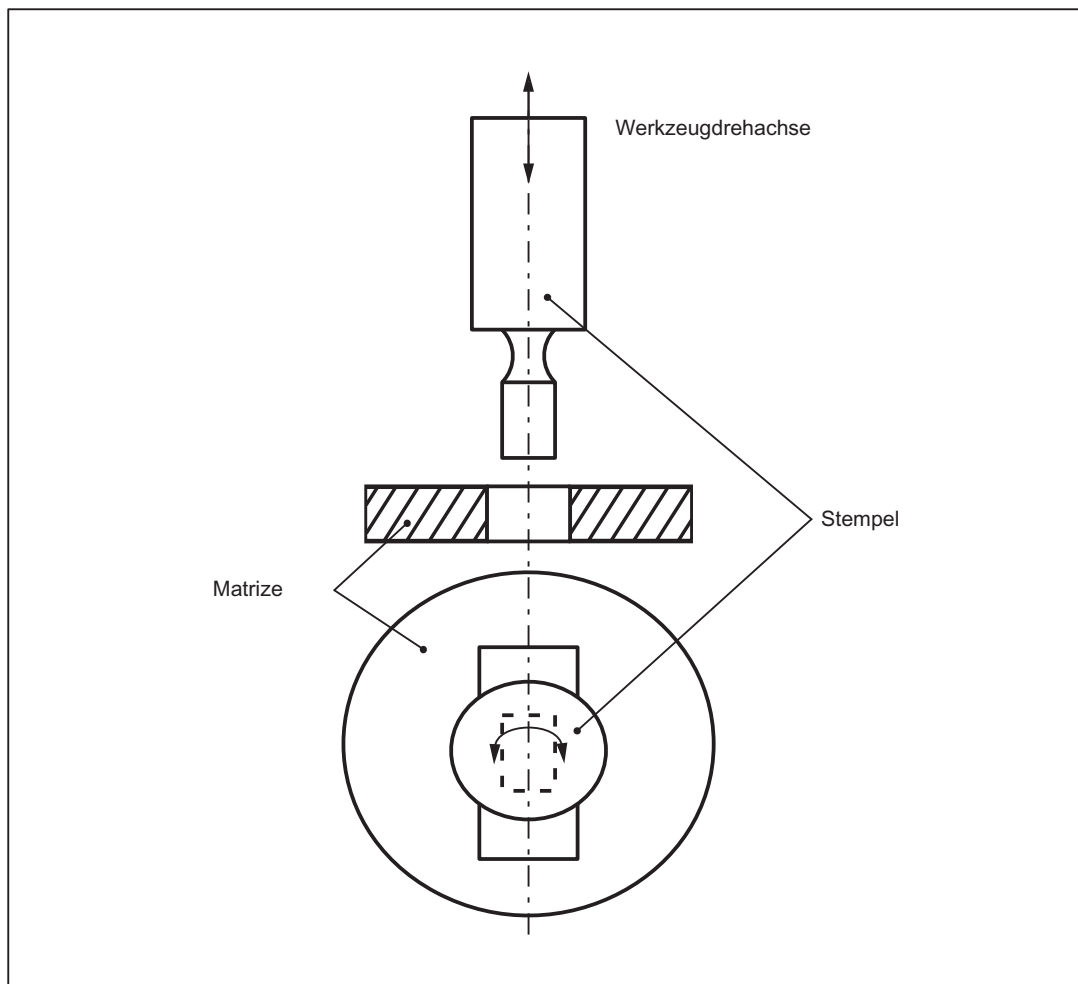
Darstellung einer drehbaren Werkzeugachse
